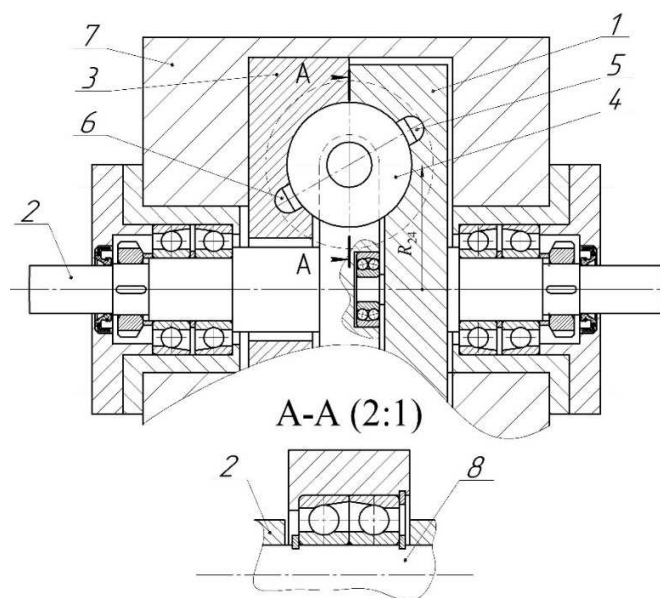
Конструкция планетарной торовой винтовой передачи со схемой установки подшипников
